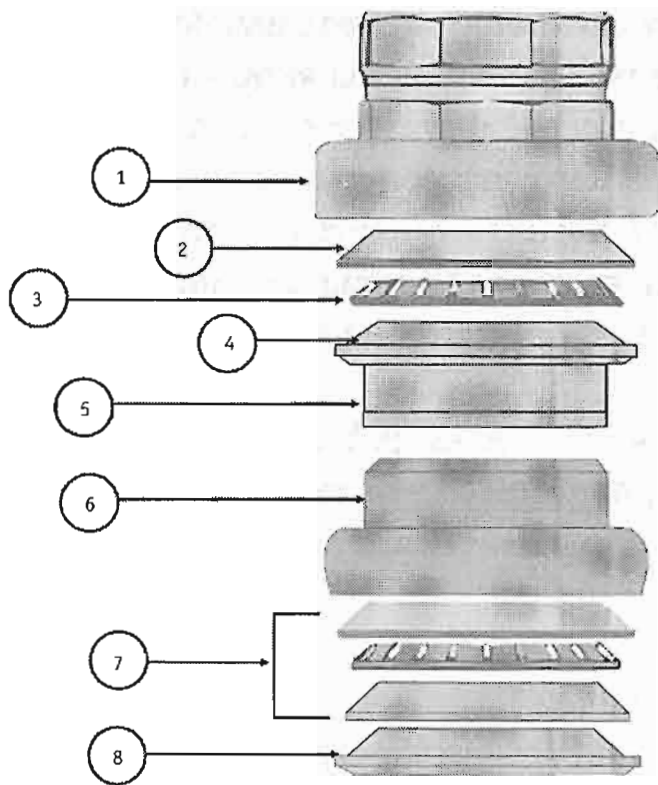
Рулевая колонка с игольчатыми подшипниками.
